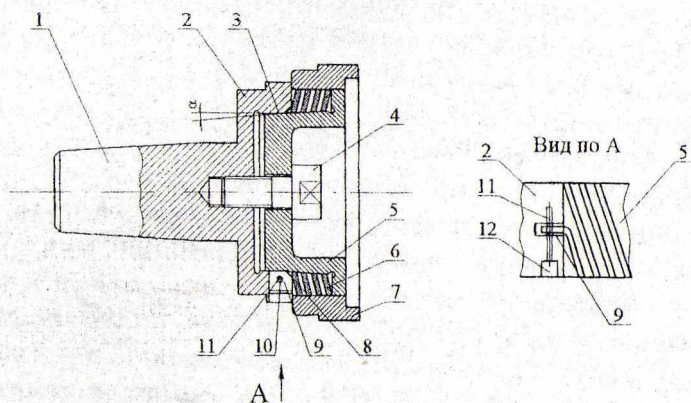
Оправка для проточування і профілювання заготовок (1- конус морзе, 2- циліндр, 3- глухий отвір, 4-болт, 5- втулка, 6- гвинтова тарілчаста пружина, 7- притискна оправка, 9- осьовий паз, 10- отвір, 11- штифт, 12- фаска).
